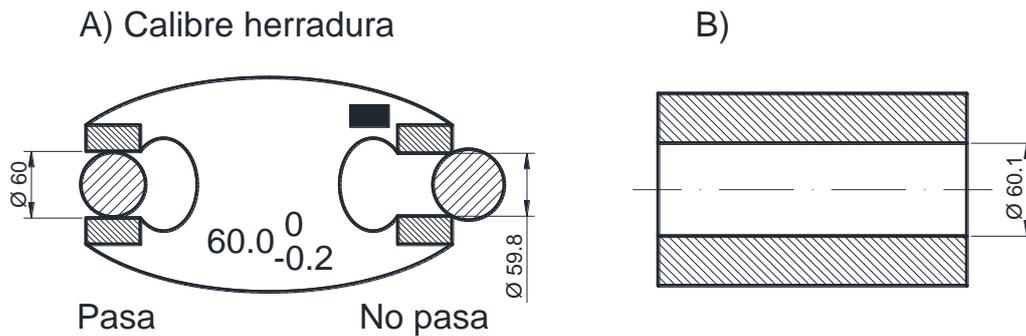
A) Calibre herradura pasa/no pasa. B) Calibre cilíndrico para verificar la tolerancia geométrica.
